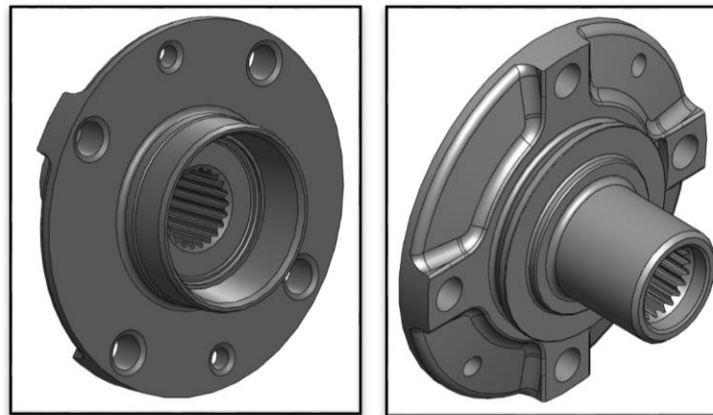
PERSPECTIVAS FRONTAL E TRASEIRA DE CUBO DE RODA
